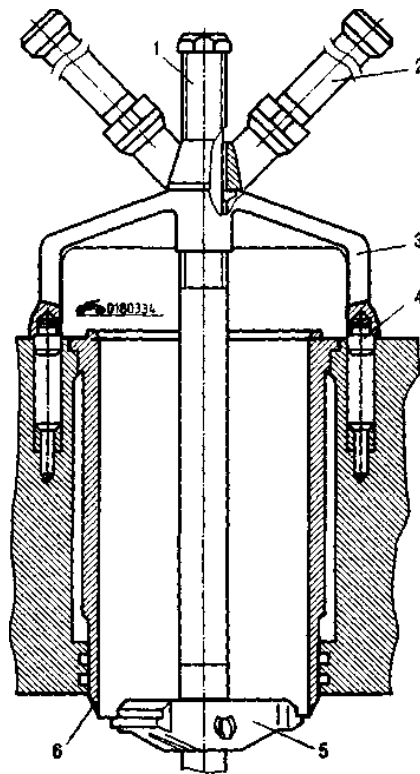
Знімач для зняття гільз: 1 – гвинт; 2 – рукоятка; 3 – корпус; 4 – опора; 5 - захоплення; 6 - гільза циліндра
